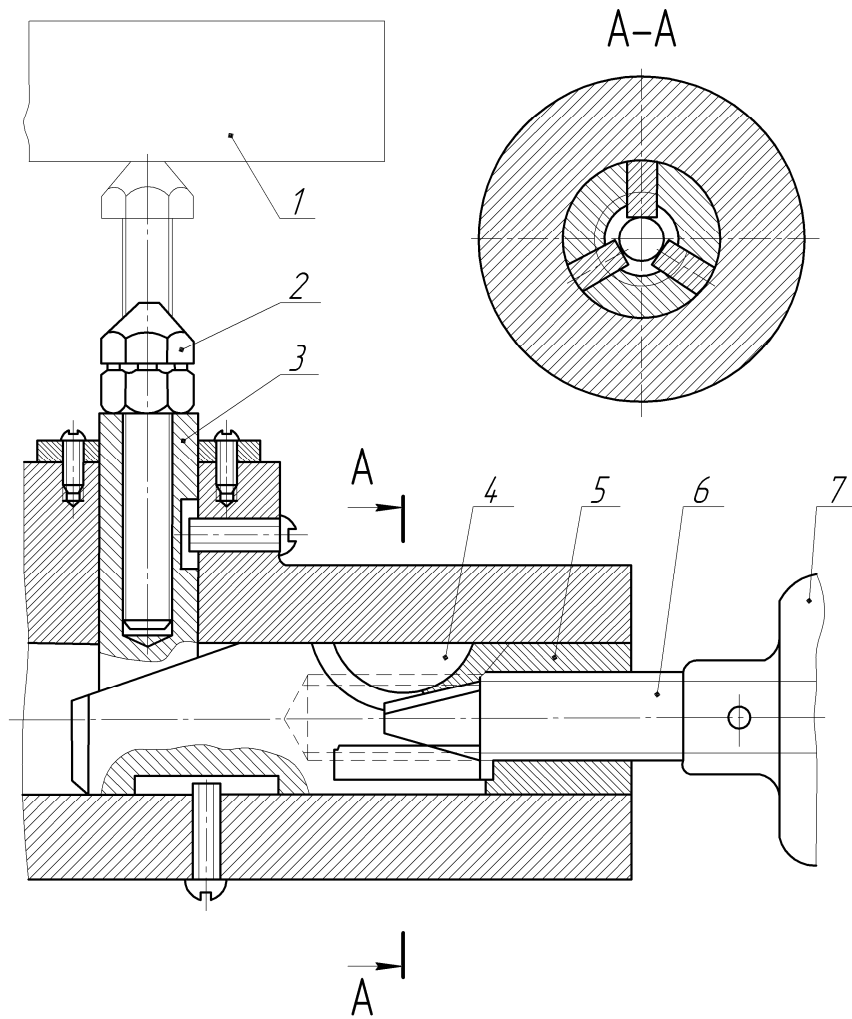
Будова підвідної клинова опори: 1 – оброблювана деталь; 2 – регульований гвинт; 3 – плунжер; 4 – шпонка; 5 – клин; 6 – гвинт; 7 – рукоятка
